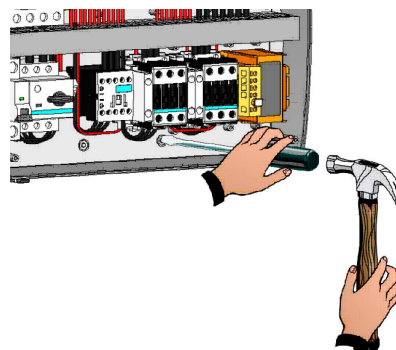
Mithilfe eines Schraubendrehers die vier vorgefertigten Löcher auf der Rückseite durchdrücken, um die vier Befestigungslöcher für das elektrische Bedientableau herzustellen.
